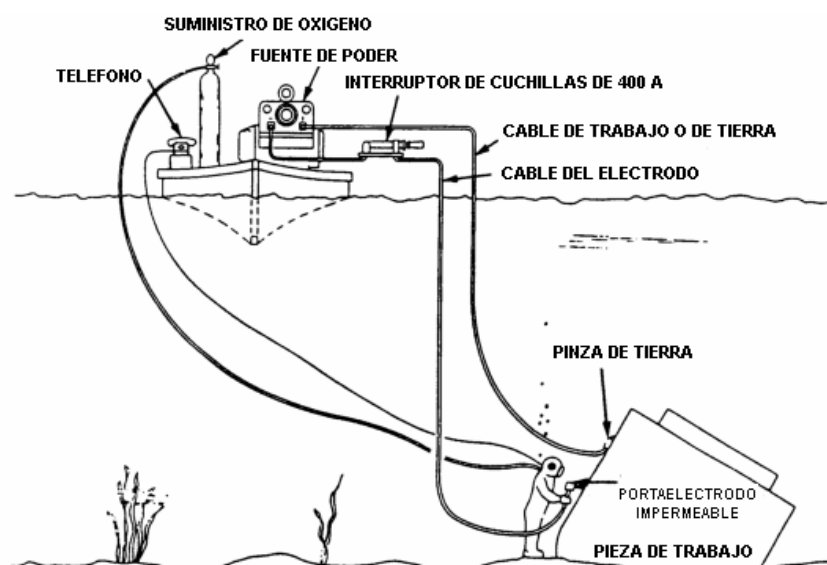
Componentes del proceso de soldadura MMA [11].
